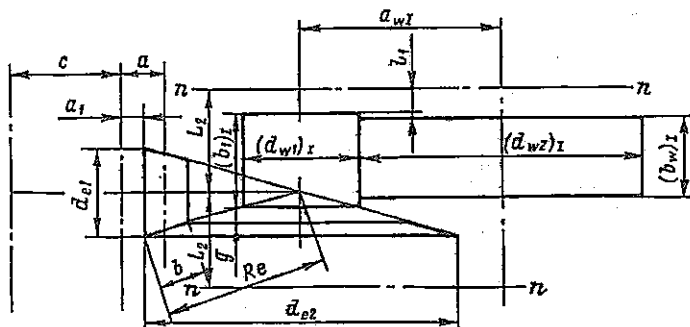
Схема расположения зубчатых колес коническо-цилиндрического редуктора
